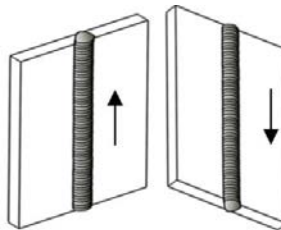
ตัวอย่างท่าเชื่อม Fillet Welding (ISO)
